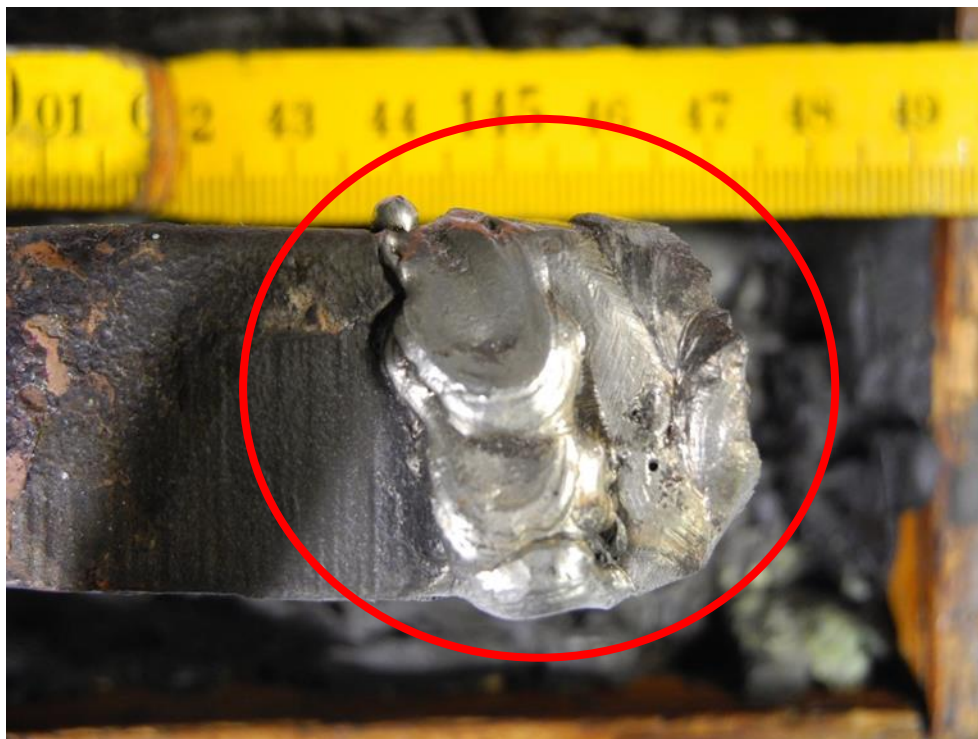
Makroaufnahme der Schweißung mit Lunker und Einbrandkerben
